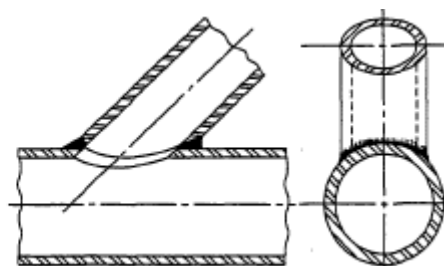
(С). Типичное сварное угловое патрубковое присоединение без дополнительного усиления.
